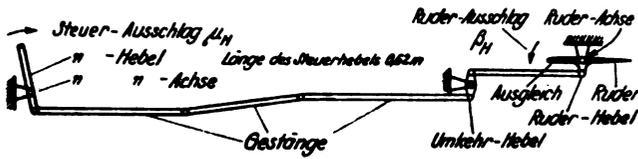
Plan der Steuerung des Flugzeuges Junkers F 13 ge.
